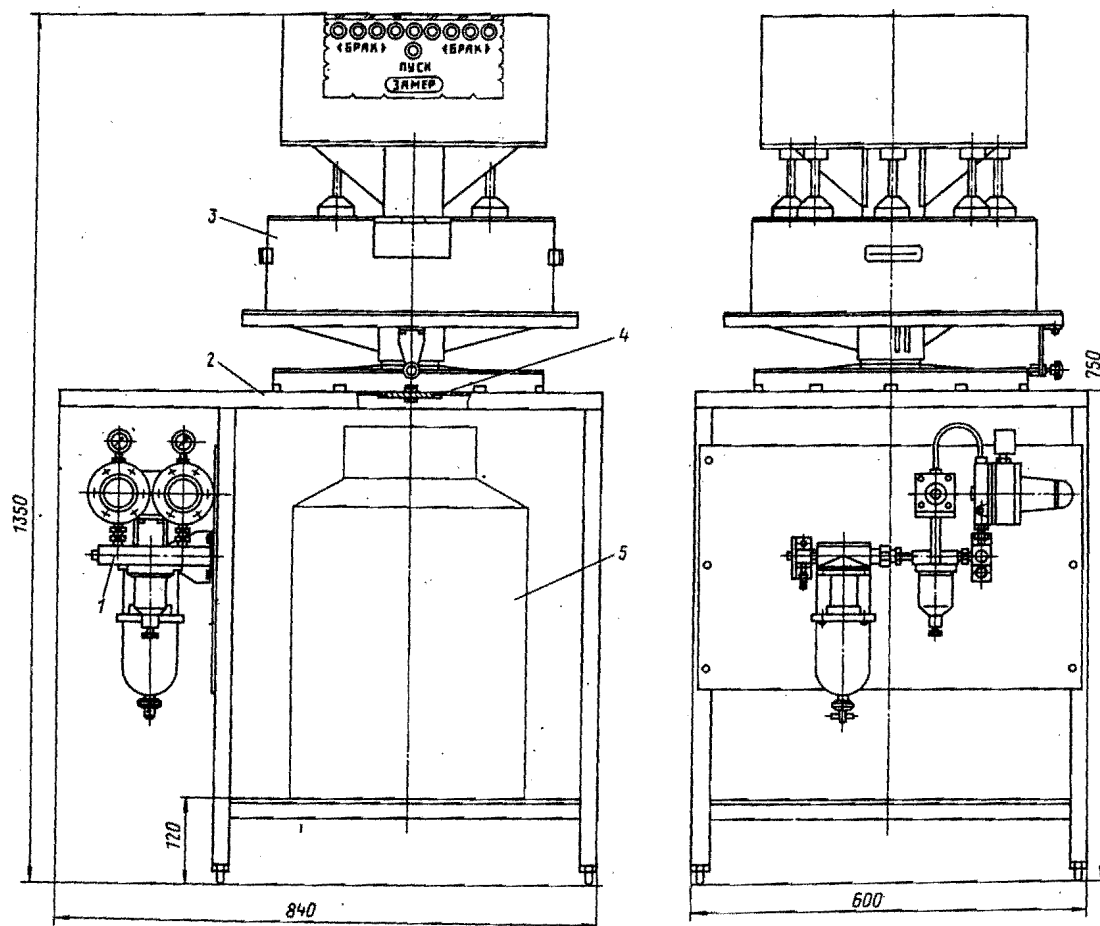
Общий вид устройства марки А1-ОГП для проверки герметичности пакетов:
